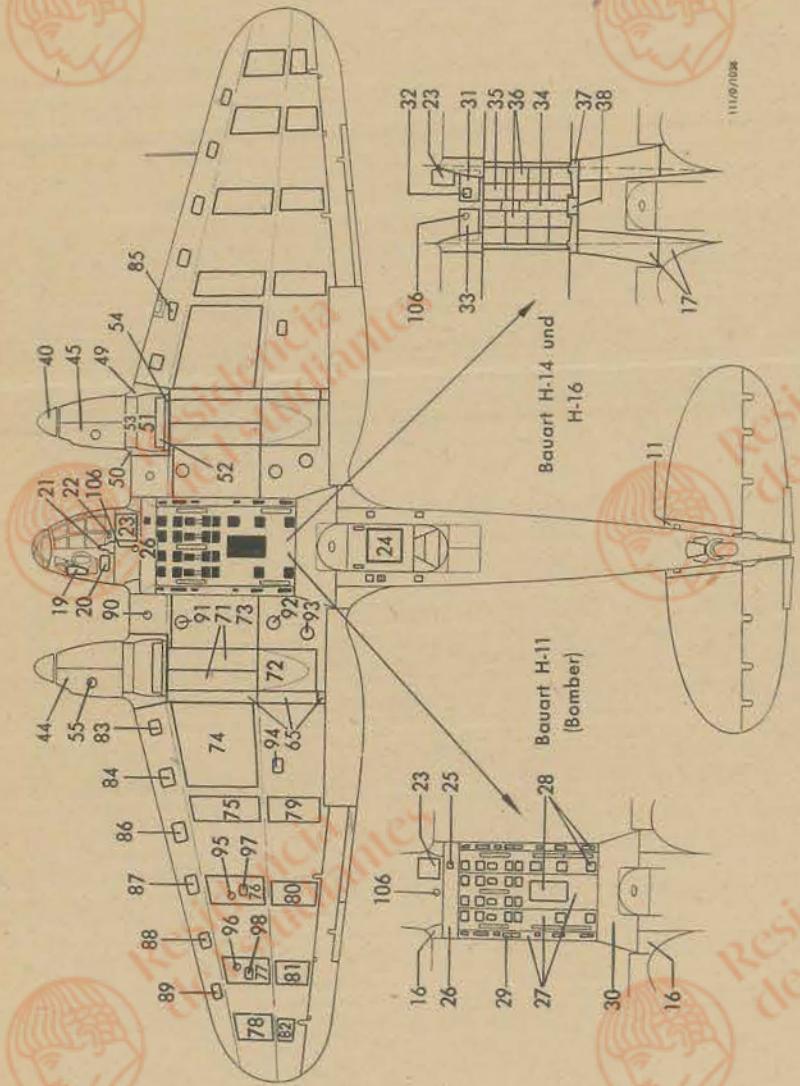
Deckel- und Klappenplan (Ansicht von unten)
